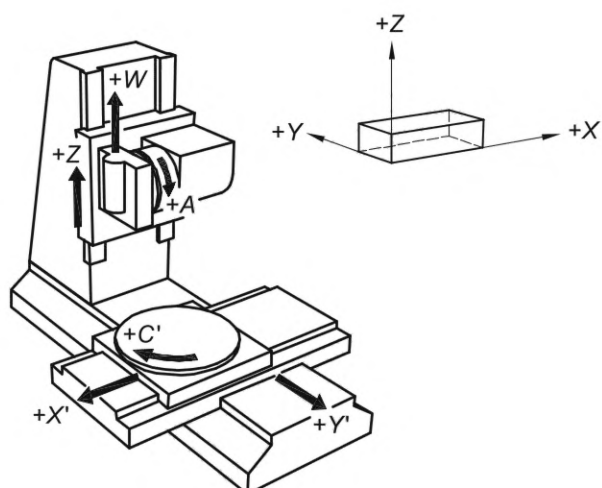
Контурно-фрезерный станок с поворотной шпиндельной бабкой
